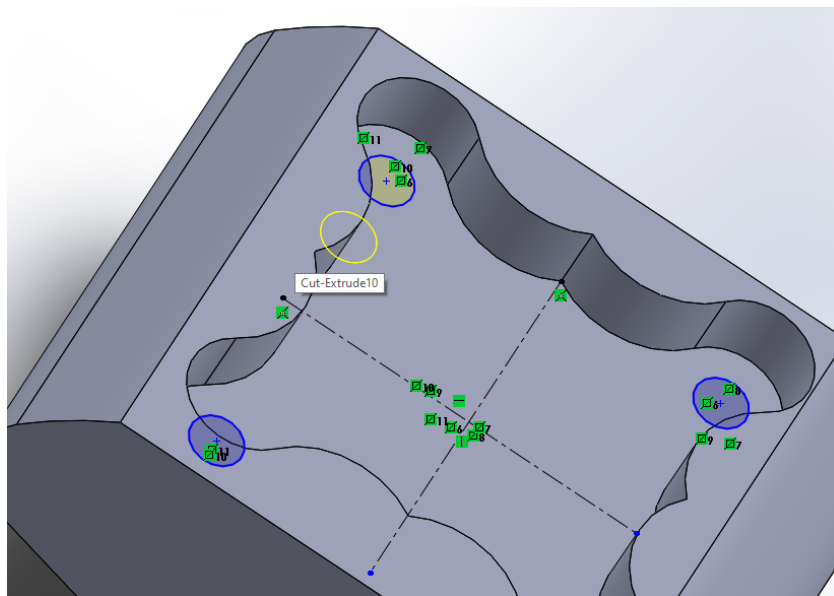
Cut-Extrude dos furos do dispositivo de fixação.
